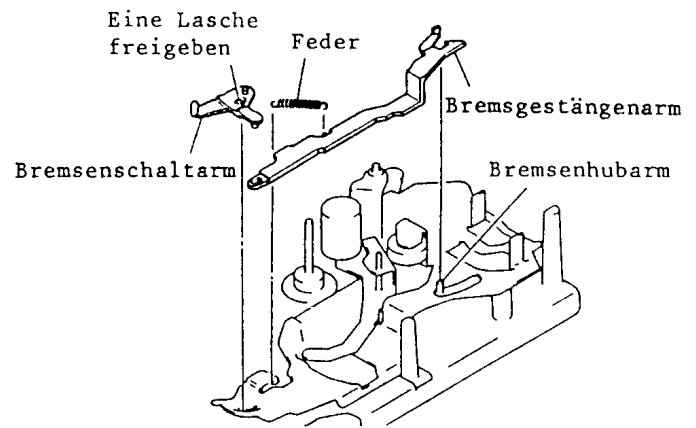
Bremsgestängearm, Bremsschaltarm
